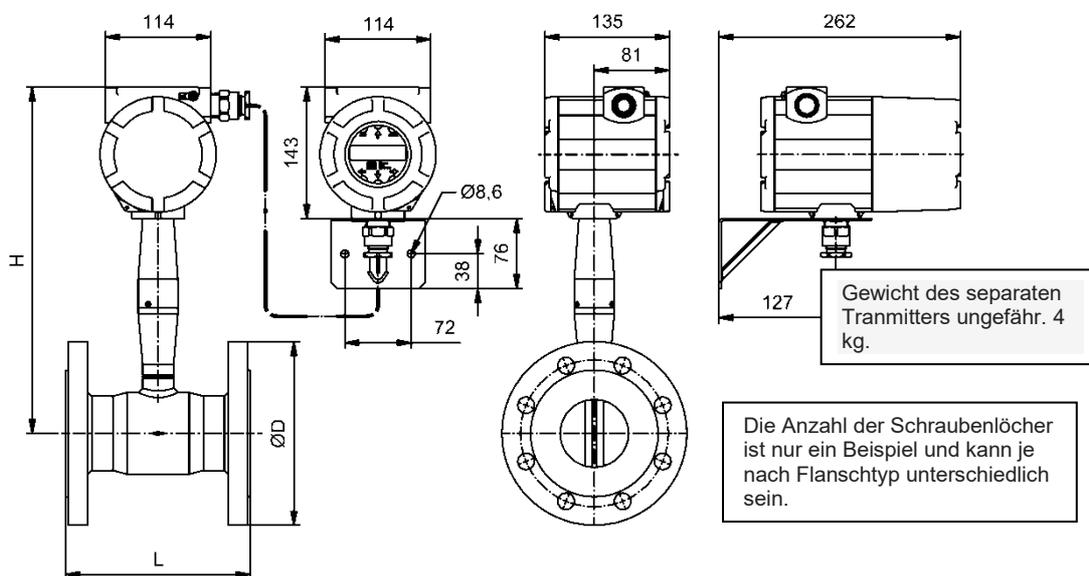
Dimensionen Flanschversion mit separater Elektronik
